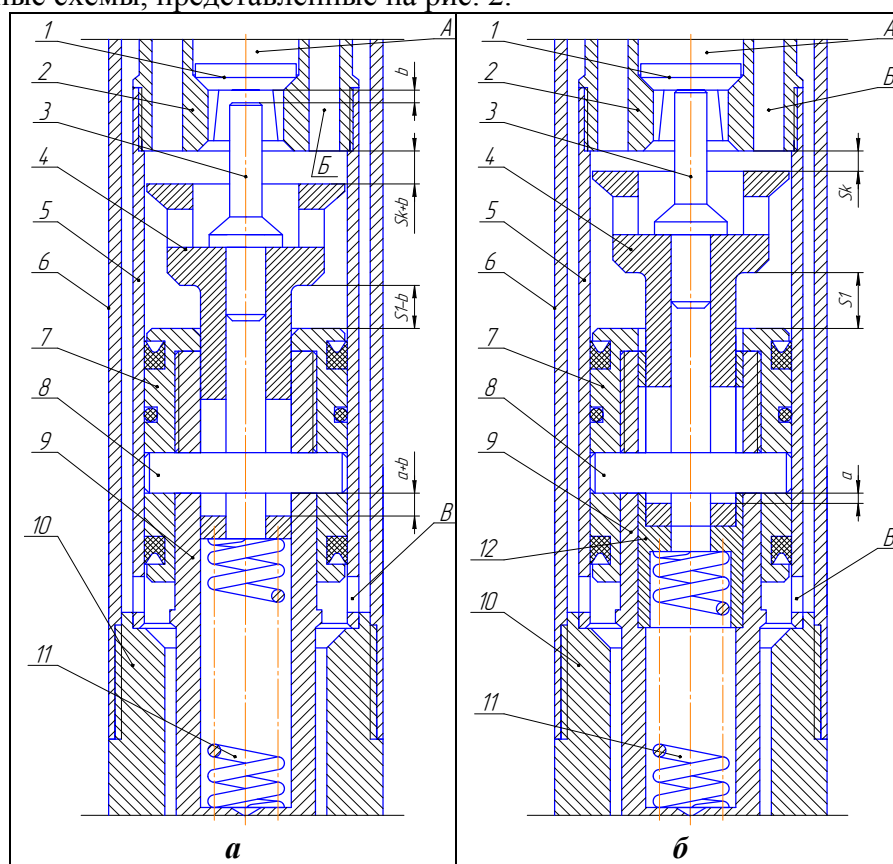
Варианты конструктивного исполнения клапанных групп гидроударников: 1 — впускной клапан; 2 — клапанная коробка; 3 — толкатель; 4 — выпускной клапан; 5 — цилиндр; 6 — верхний корпус; 7 — поршень; 8 — палец; 9 — боек; 10 — верхняя наковальня; 11 — пружина; 12 — втулка; *A* — впускное окно; *B* — выхлопные каналы; *B* — впускные отверстия; *S1* — рабочий ход бойка; *Sk* — ход клапанов; *a* — регулировочный зазор (определяет свободный ход бойка при движении вниз); *b* — зазор между толкателем и впускным клапаном
